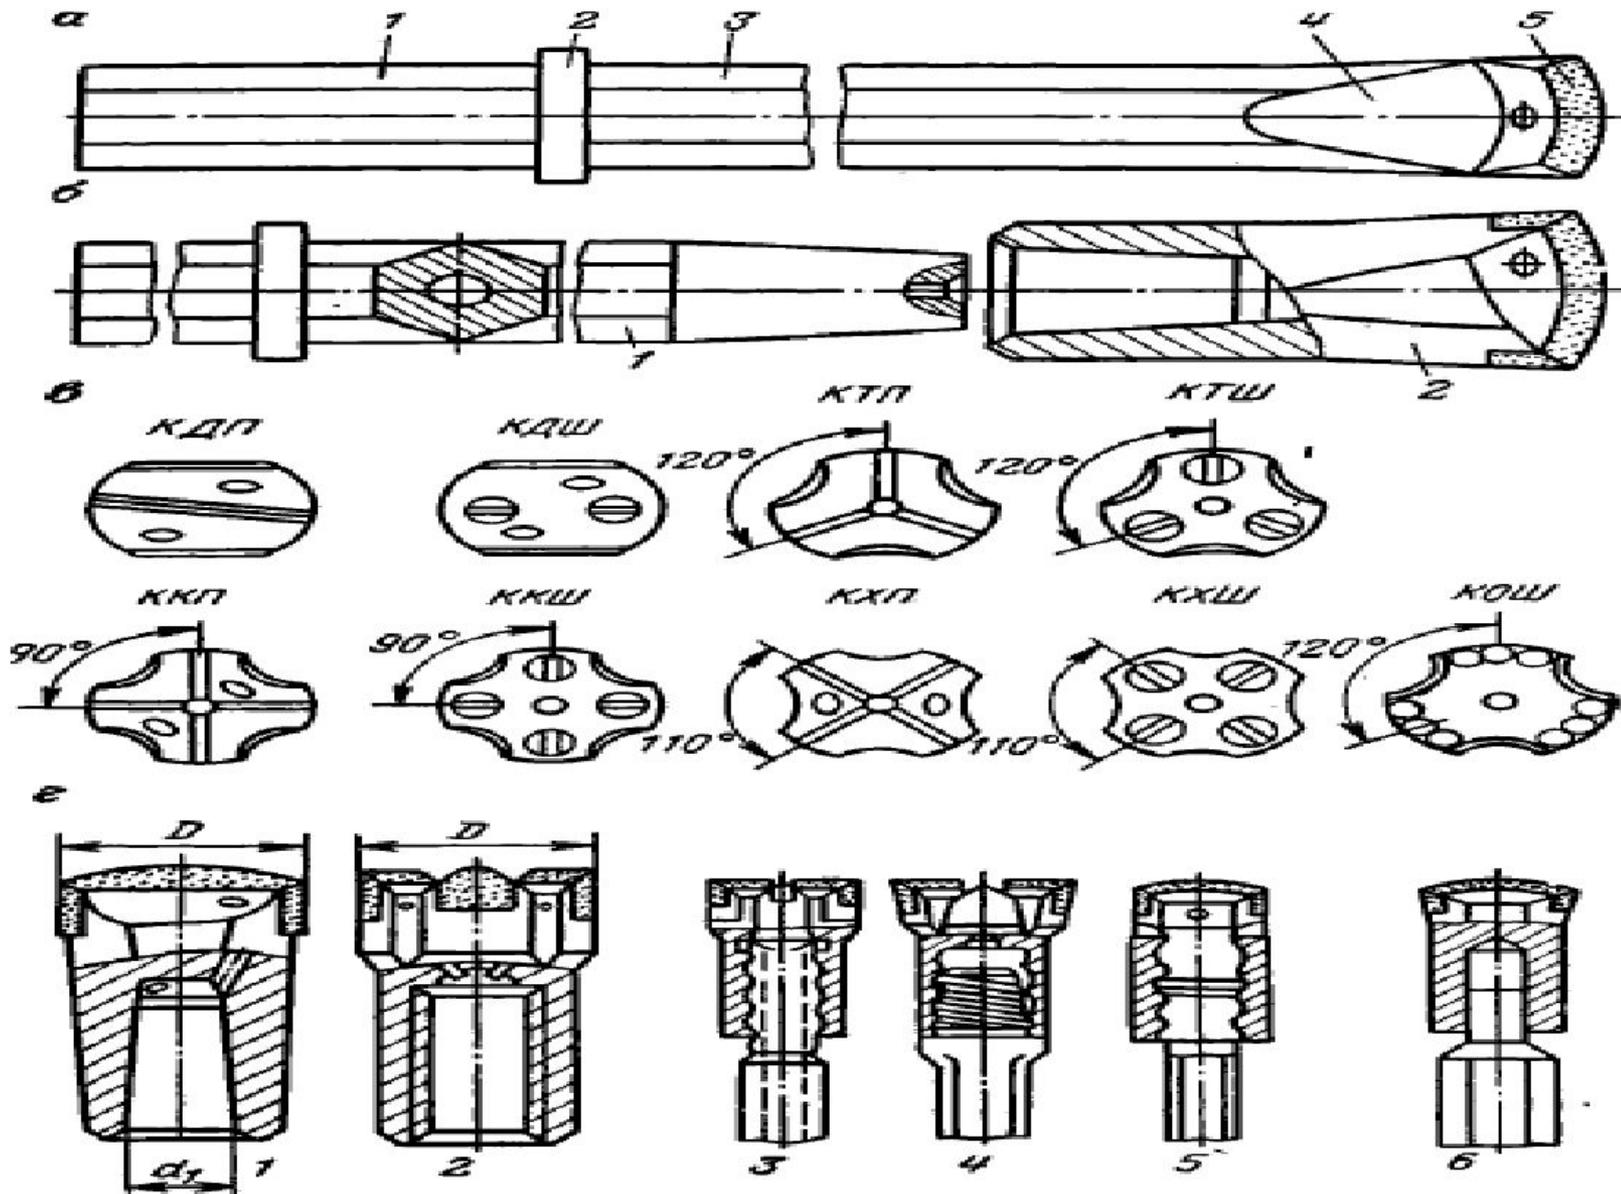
Буры и буровые коронки: а - цельный бур; б - буровая штанга с коронкой; в - типы буровых коронок; г - виды соединений.
